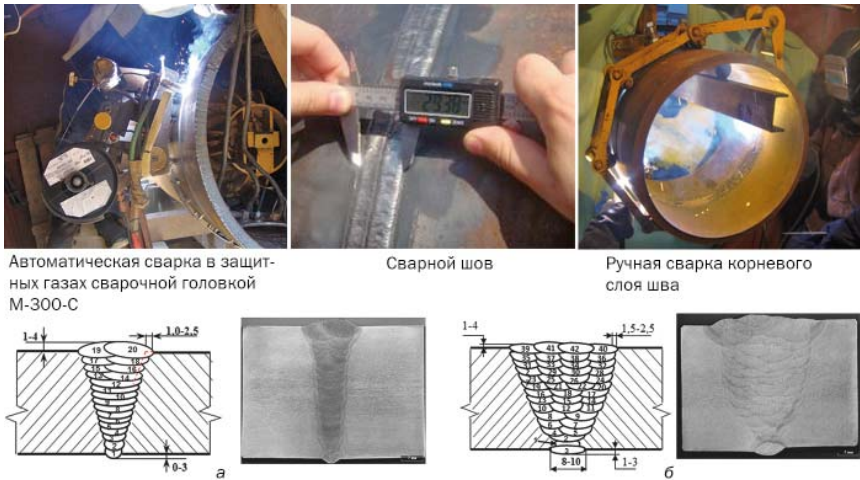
Квалификационные испытания технологии сварки кольцевых стыковых соединений и макрошлиф сварного соединения труб Ду1219 × 41,0 мм, выполненного автоматической (а) и ручной дуговой (б) сваркой при строительстве сухопутного участка морского газопровода «Nord Stream»
